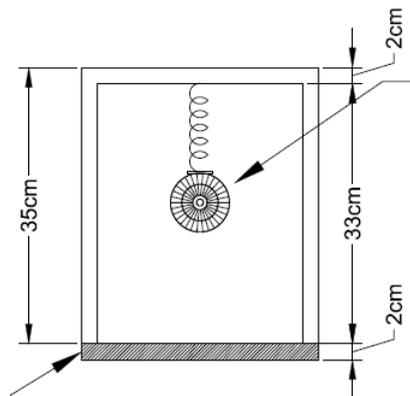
Vista frontal da mola e motor acoplados à base de ferro.
